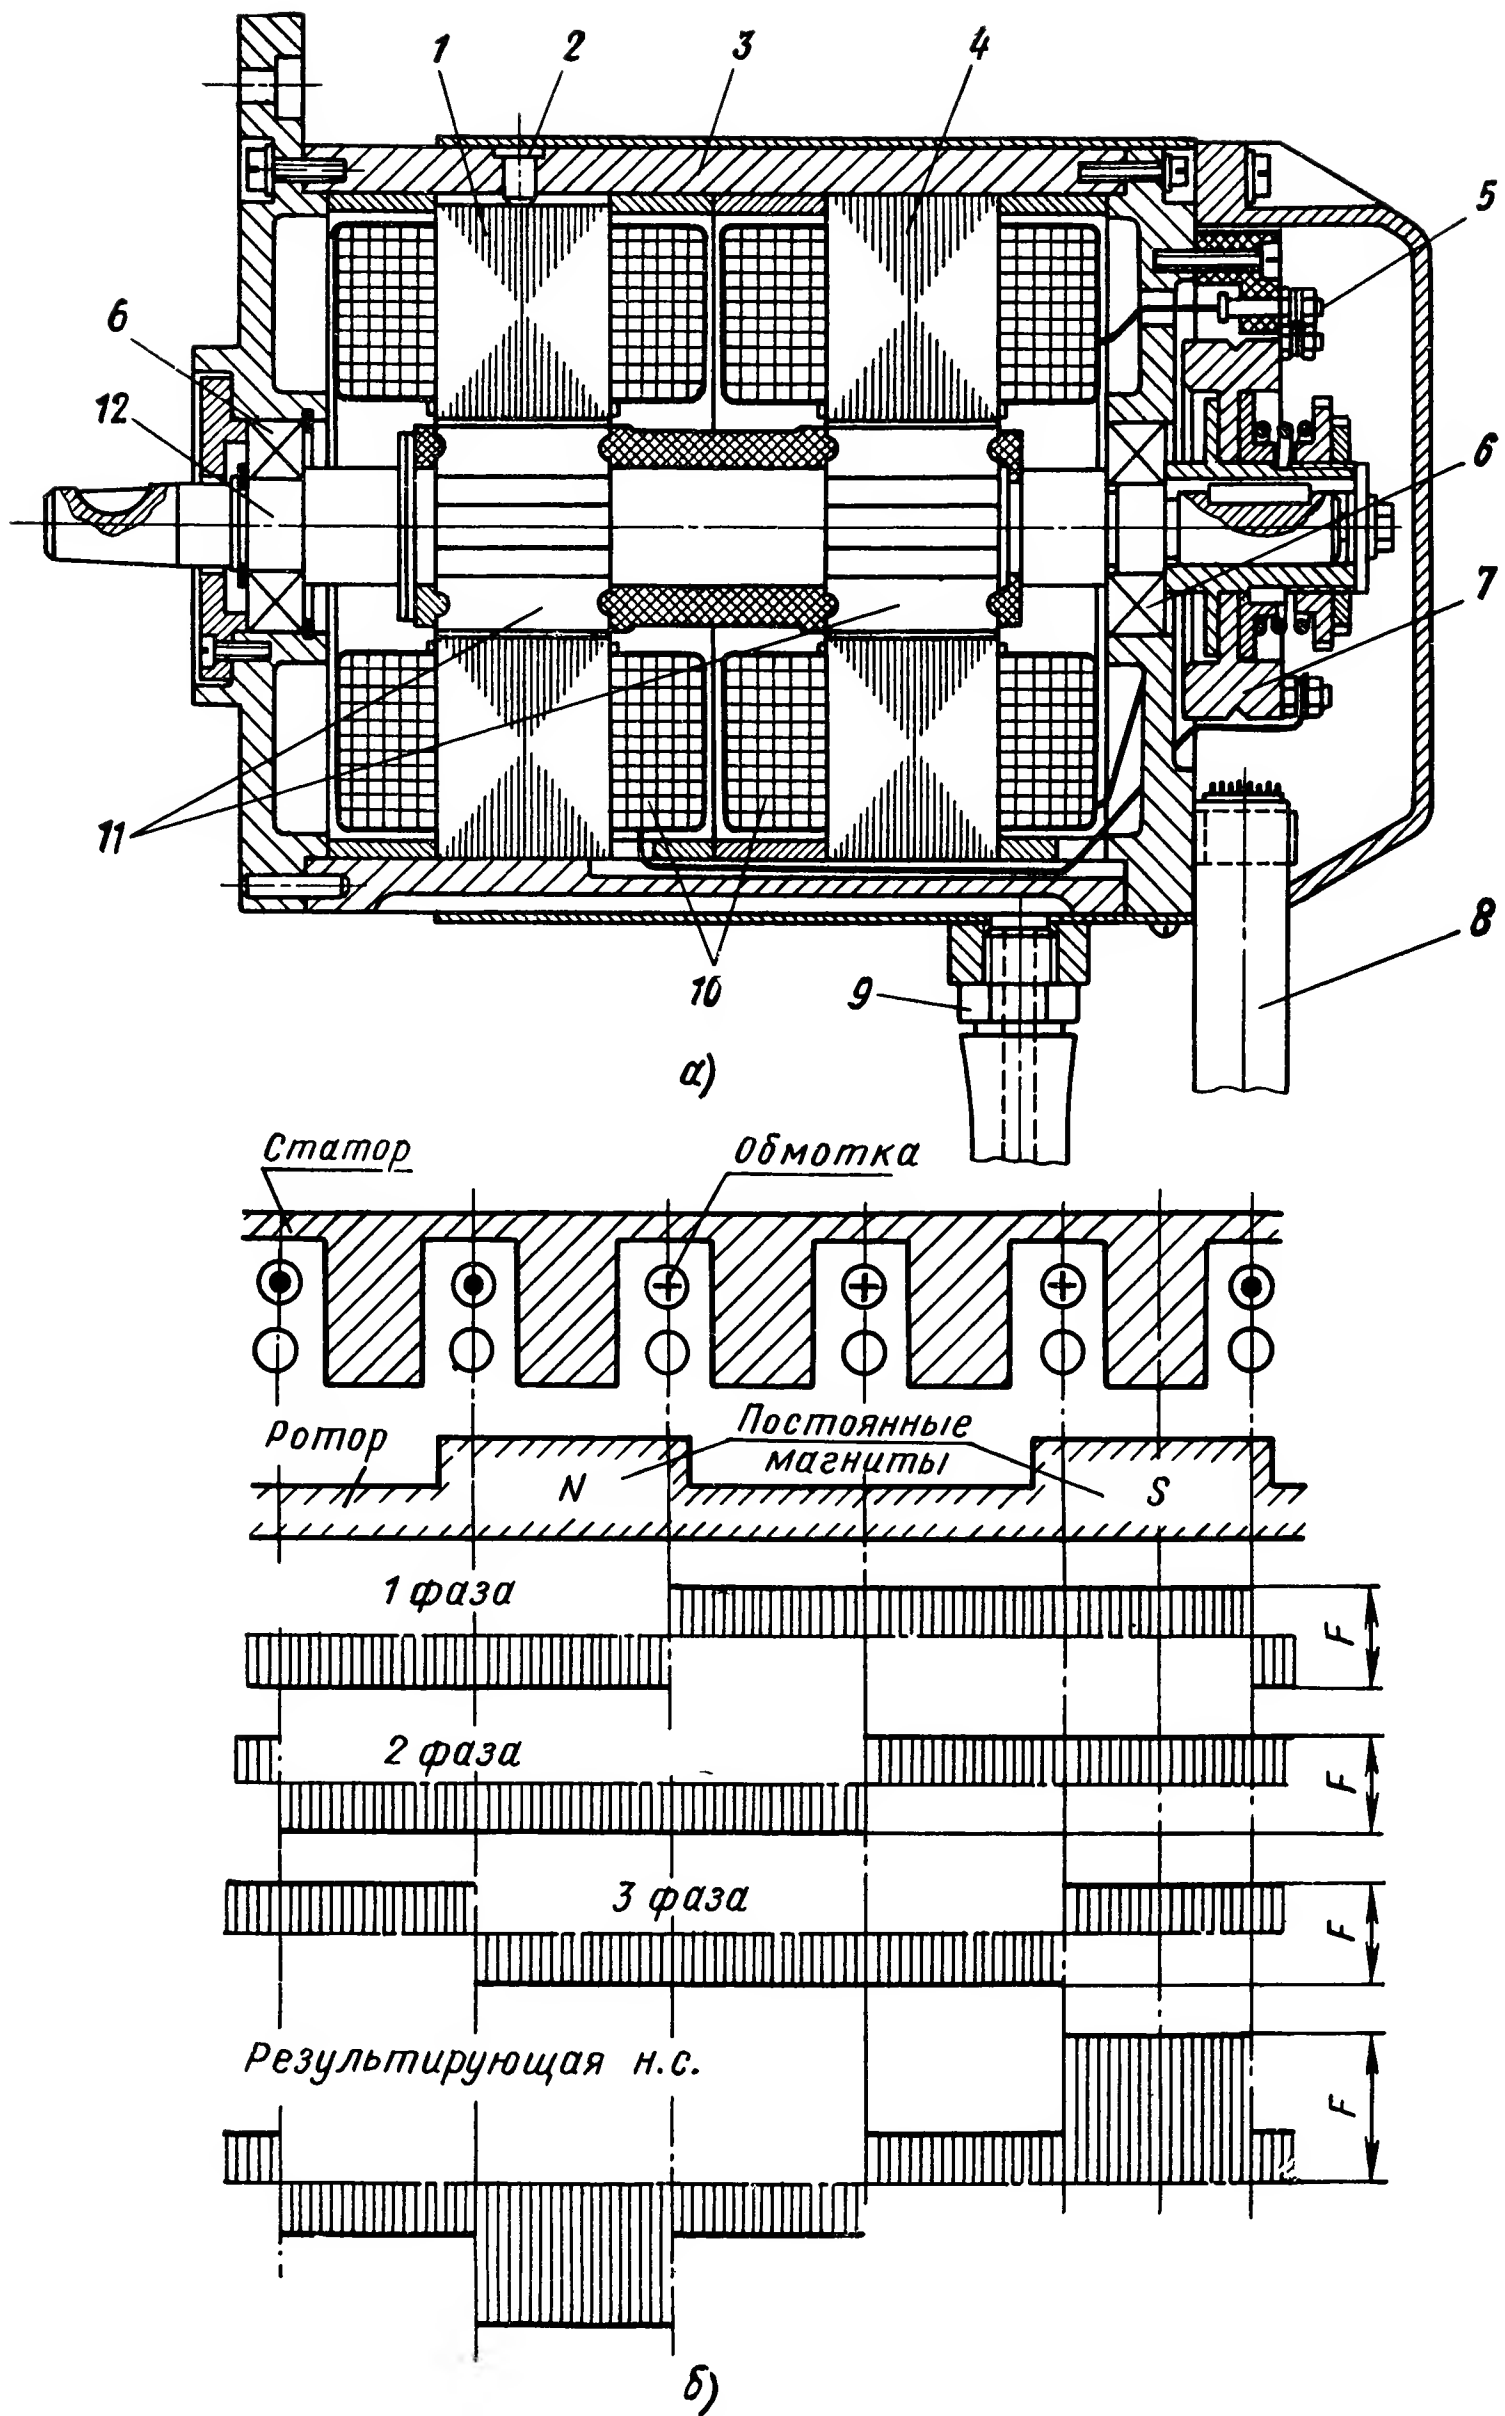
Двухпакетный магнитоэлектрический шаговый двигатель:
